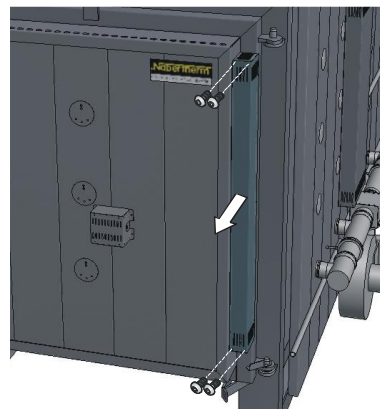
Exemplo: Terminais dos elementos de aquecimento (semelhante à figura)
